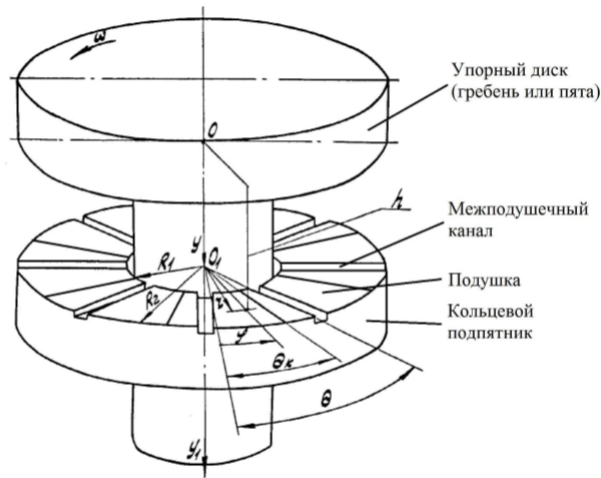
Общий вид одностороннего упорного подшипника скольжения с неподвижными подушками
